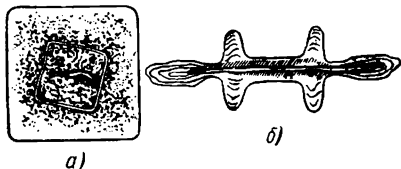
Образование расслоения в поковке шатуна: а — заготовка с дефектом перед штамповкой; б — выжимание дефекта в заусенец при штамповке
